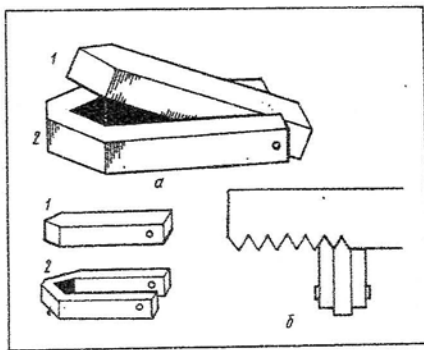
Станок для насечки зубьев пил: а — общий вид; б — насечка зубьев пилы; 1 — пуансон; 2 — матрица
